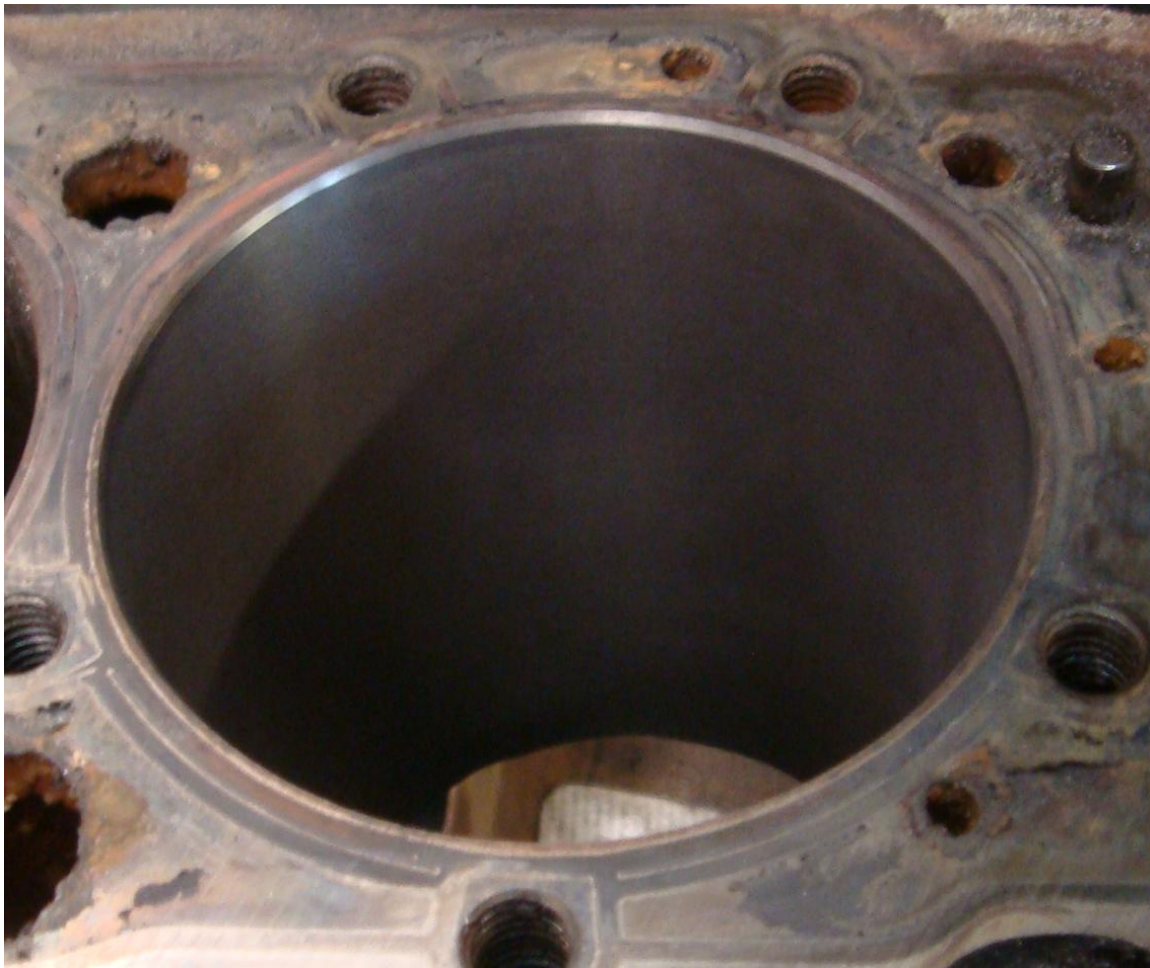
Un cilindro maquinado en mandrinadora con una profundidad de corte de 0.003". Las zonas grises revelan que el cortador ha arrancado material del cilindro. Las partes desgastadas se ven oscuras, pues la herramienta no puede cortar material más allá del diámetro que se fija en el micrómetro.
